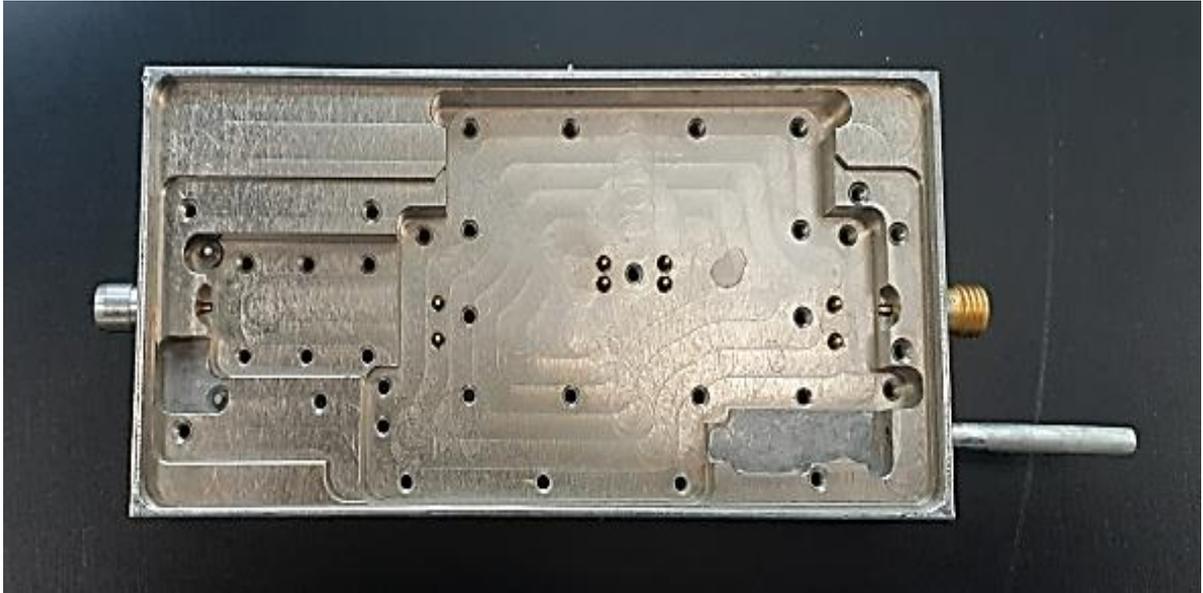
Типовой корпус микросборки после нанесения покрытия
